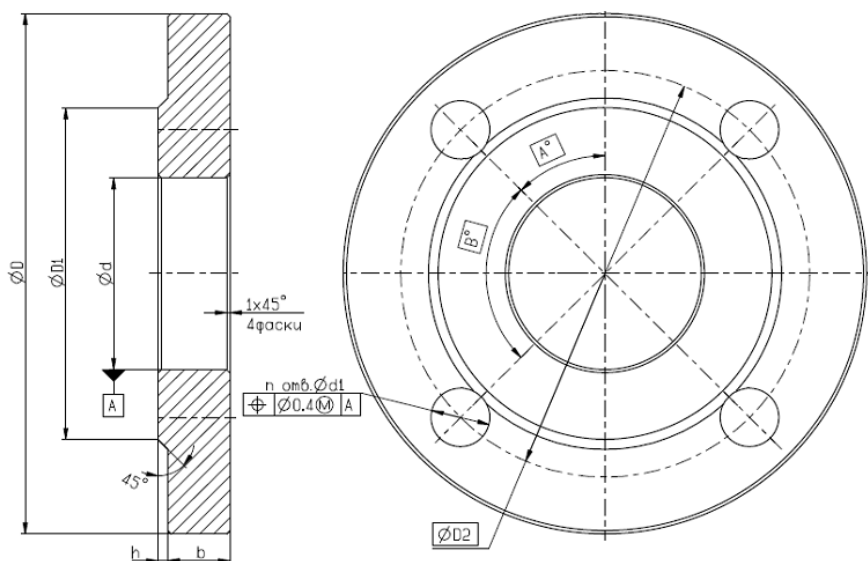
Габаритные и присоединительные размеры монтажных фланцев
